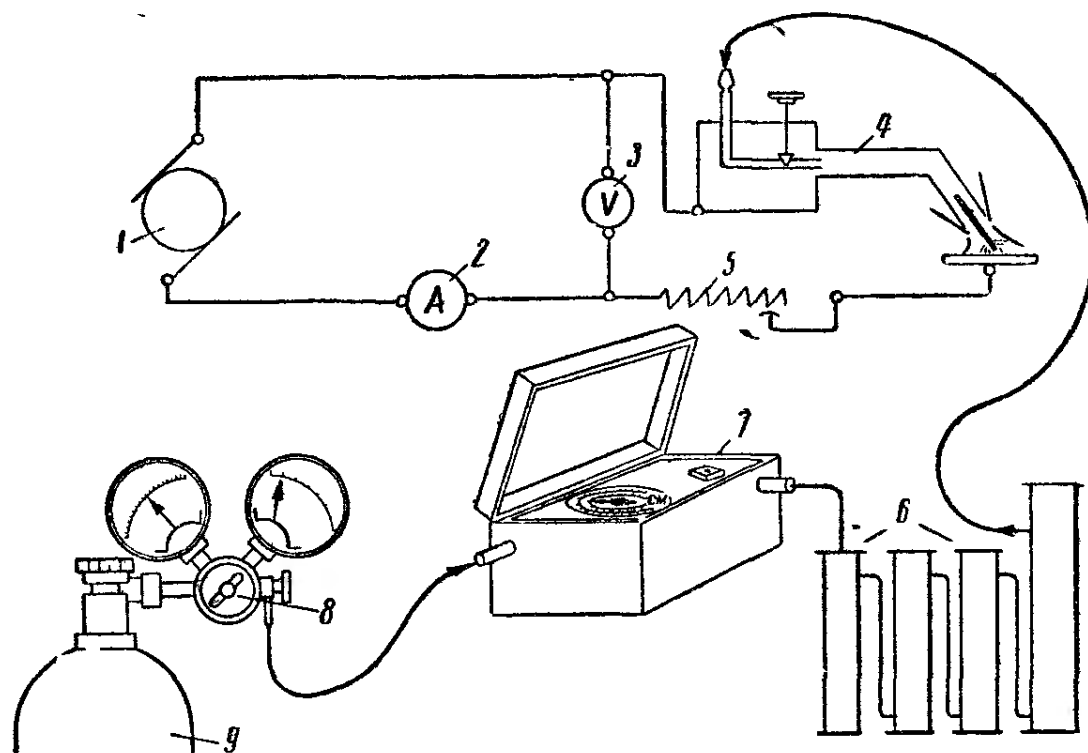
Схема установки для аргоно-дуговой сварки на постоянном токе
